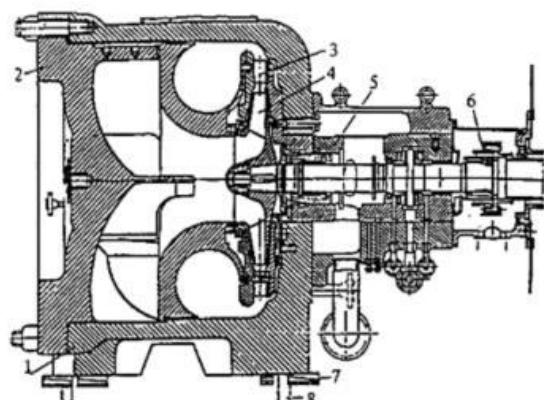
Неполнонапорный одноступенчатый нагнетатель 370-18 агрегата ГТК-10-4
